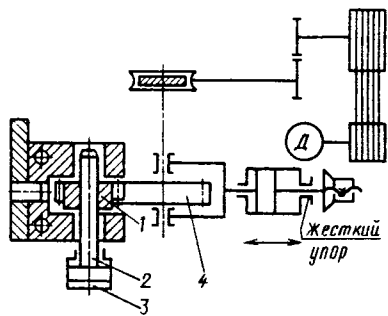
Схема процесса прикатывания зубьев цилиндрических зубчатых колес
